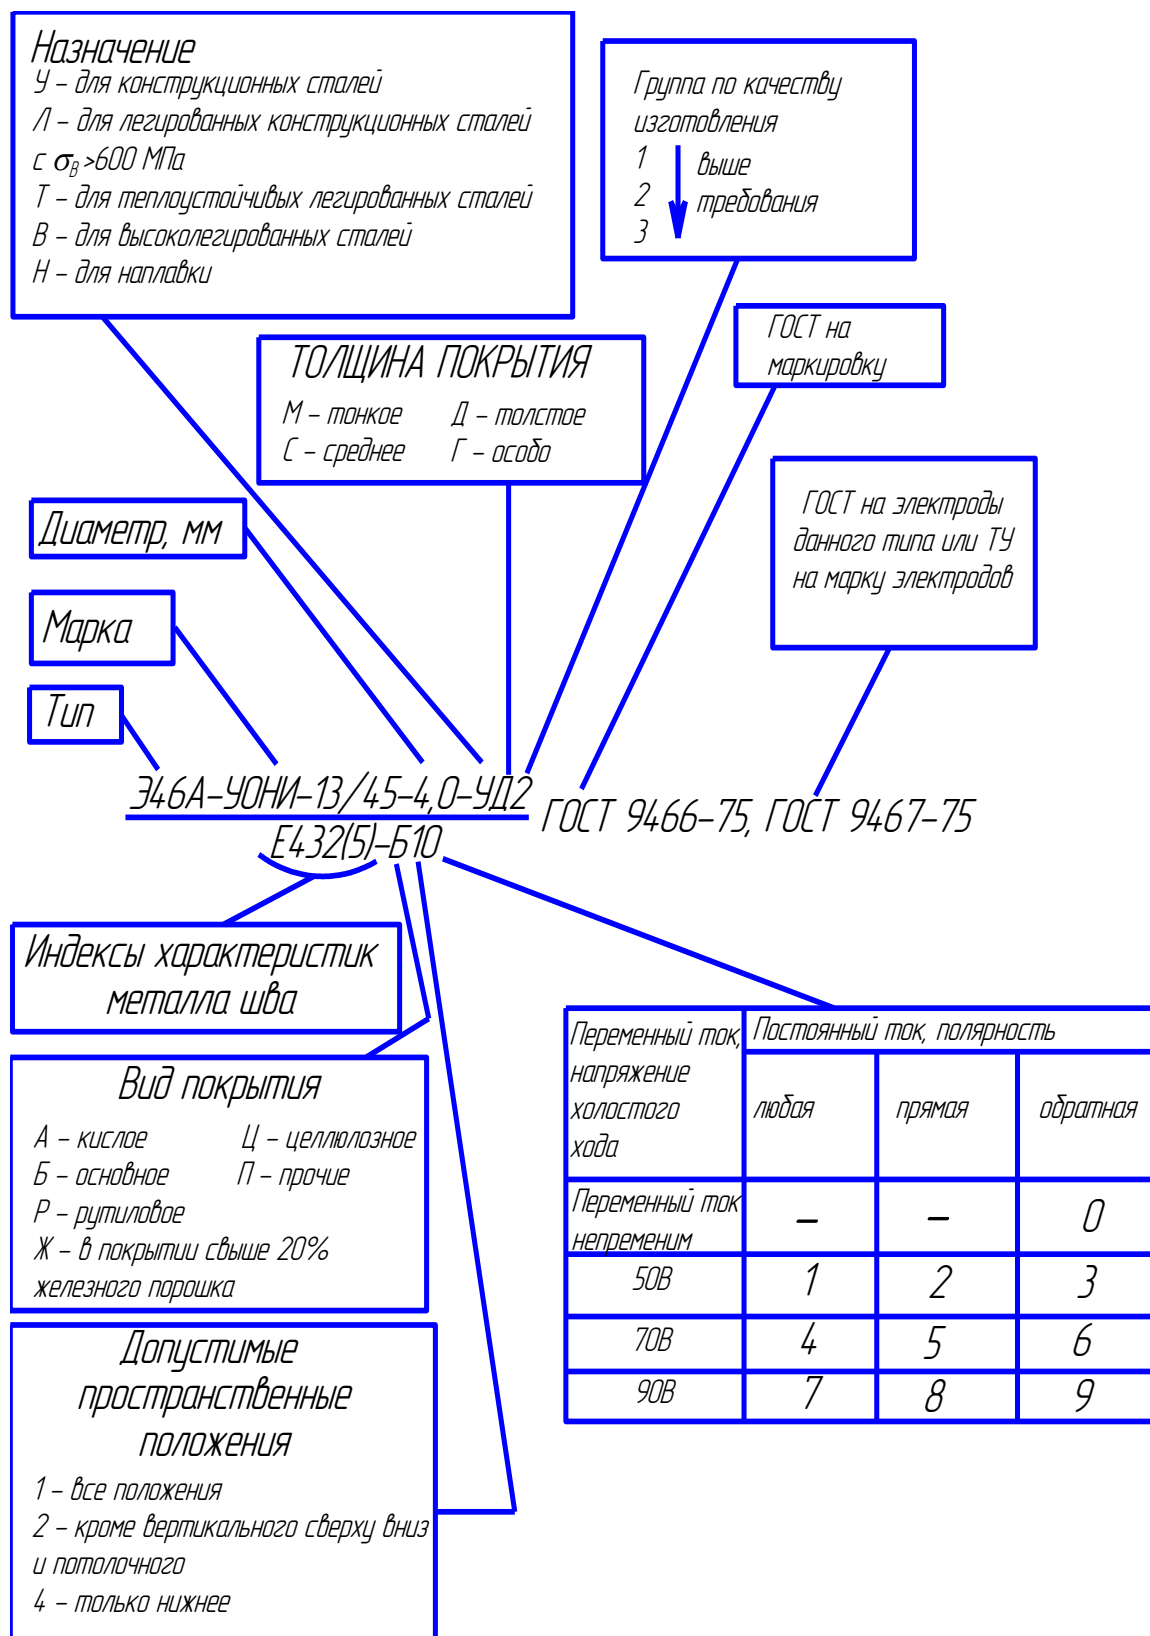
Условное обозначение электродов для сварки и наплавки
